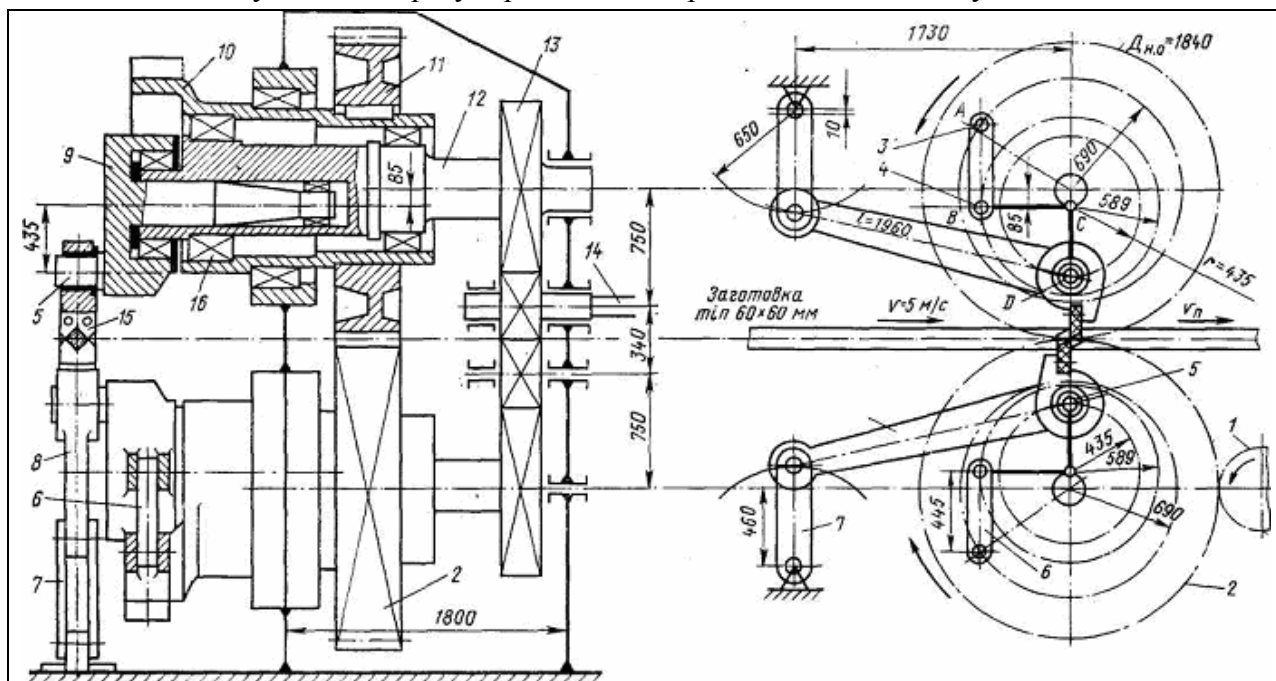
Схема кривошипно-шатунных летучих ножниц для горячей резки толстых заготовок: 1,2,11 – шестерни привода водил; 3,4 – оси водил; 5 – пальцы; 6 – серьги; 7 – качающиеся серьги; 8 – шатуны; 9 – кривошипы; 10 – водила; 12 – валы; 13,14 – привод валов 12; 15 – ножи; 16 – роликоподшипники
